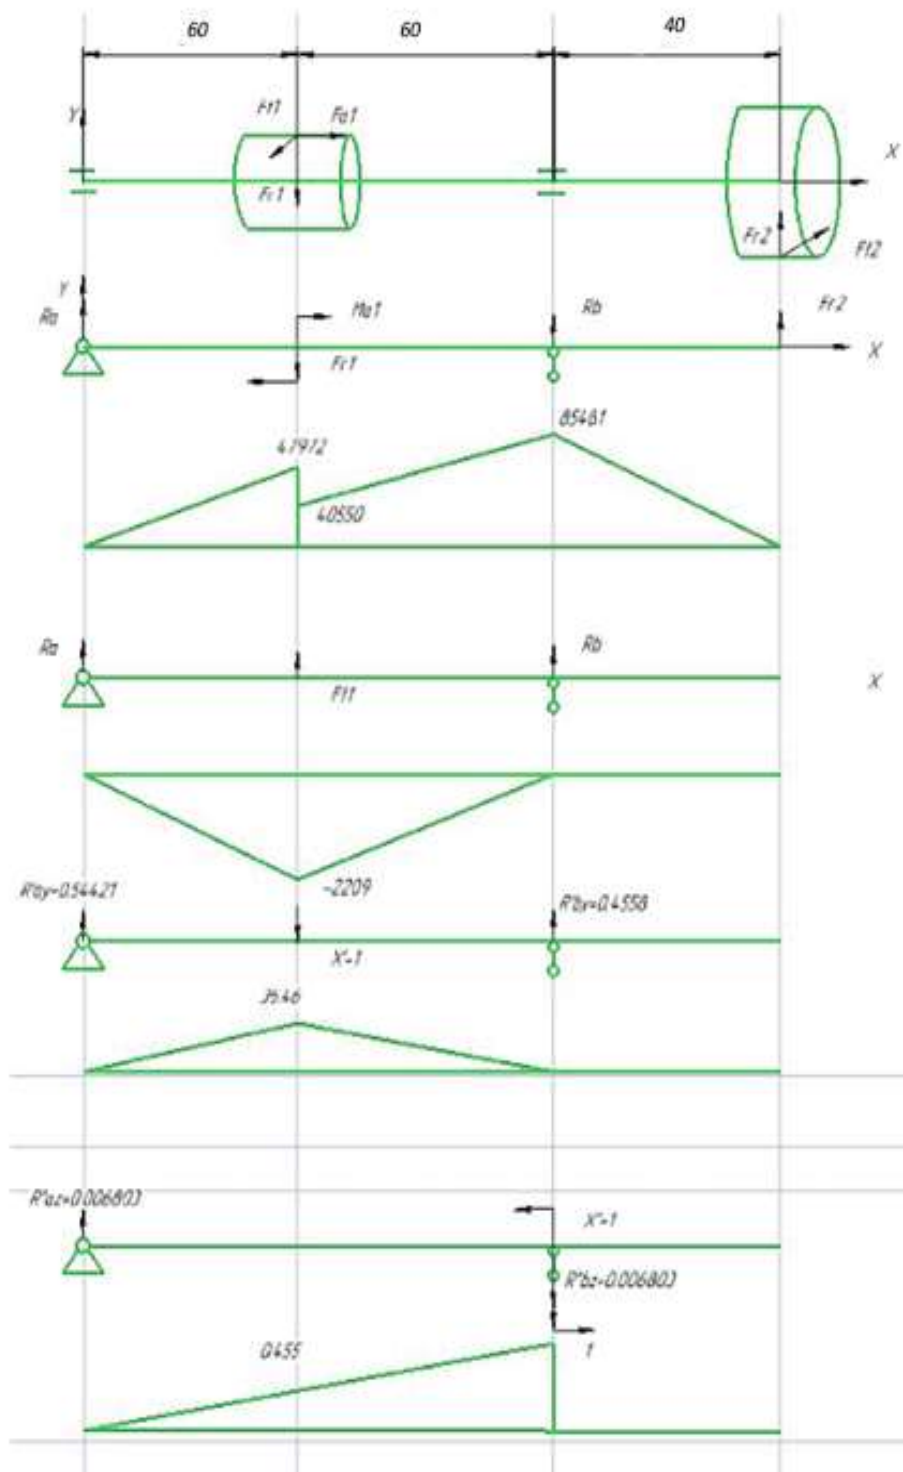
Розрахункові схеми швидкохідного вала редуктора
